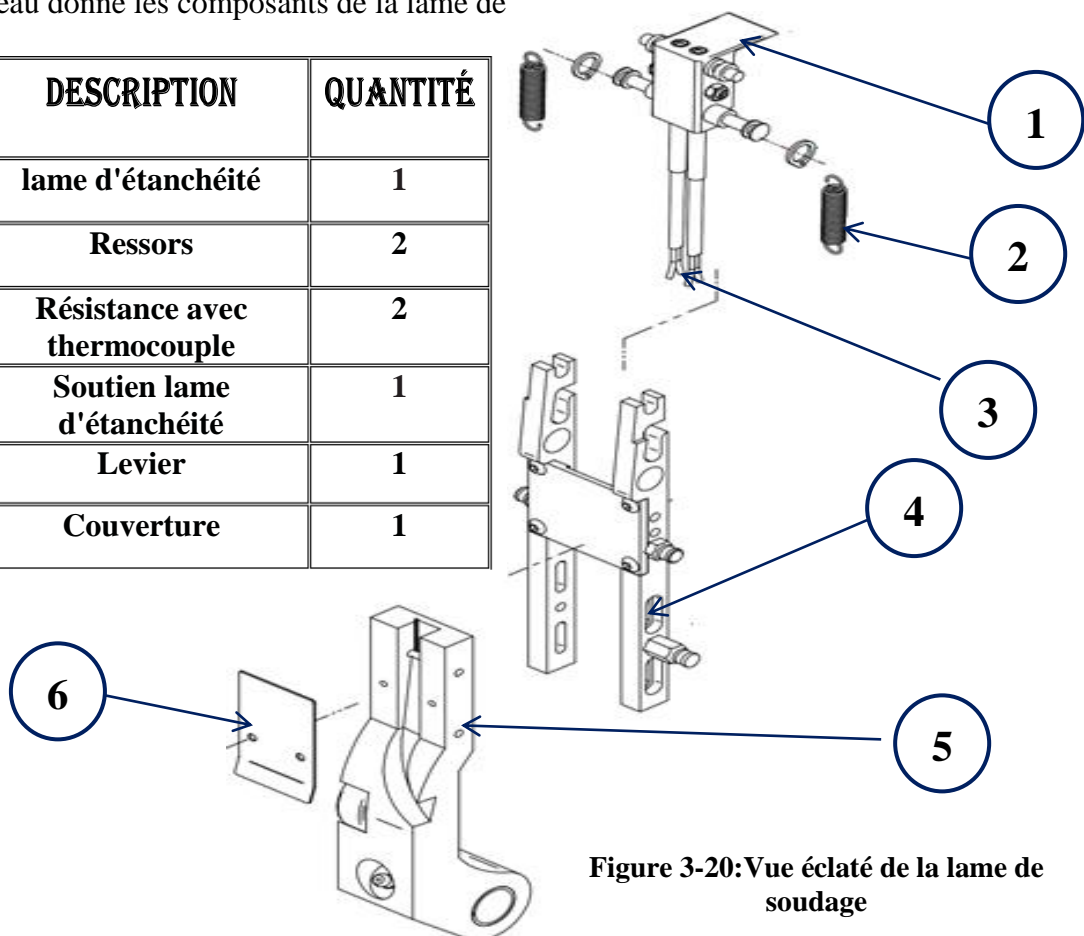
Vue éclaté de la lame de soudage
